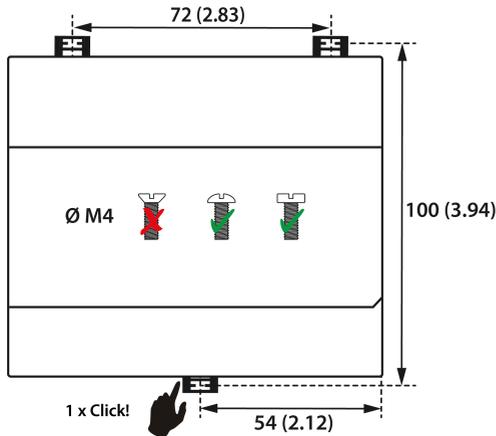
Schraubmontage; Maße in mm (in)
